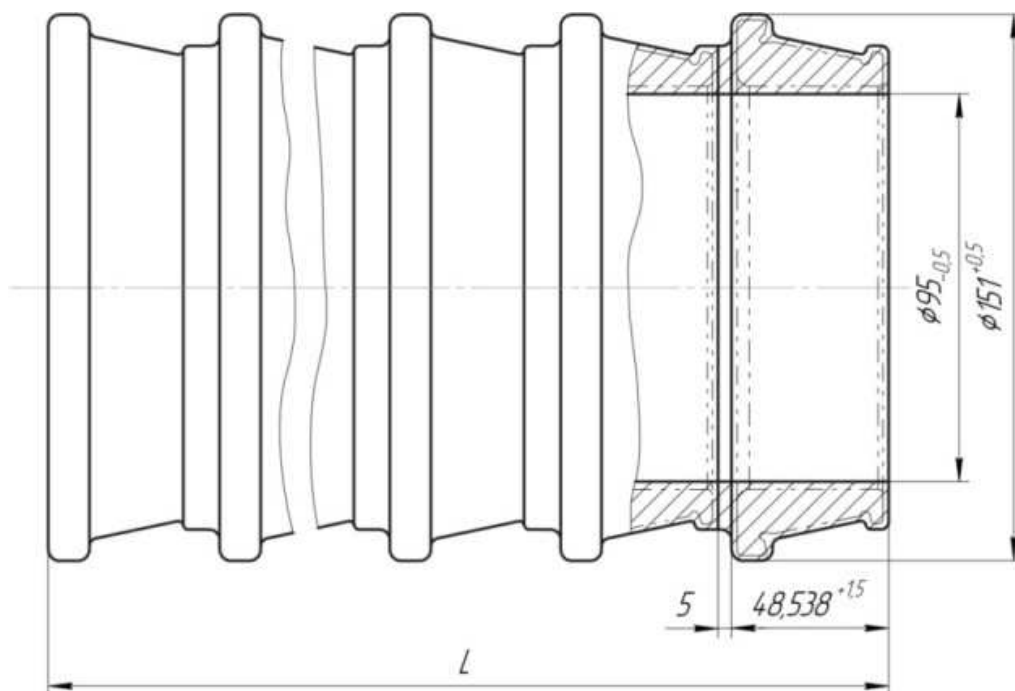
Вид трубной заготовки с РПП для механической обработки (ВК)
